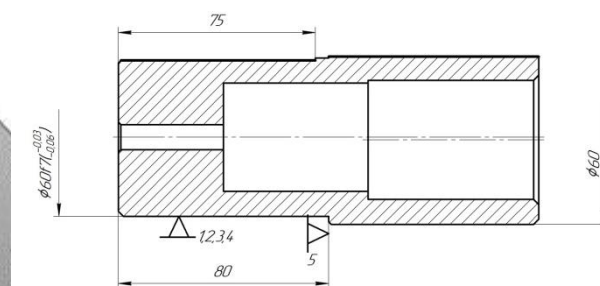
Схема базування заготовки на фрезерній операції II варіант.
